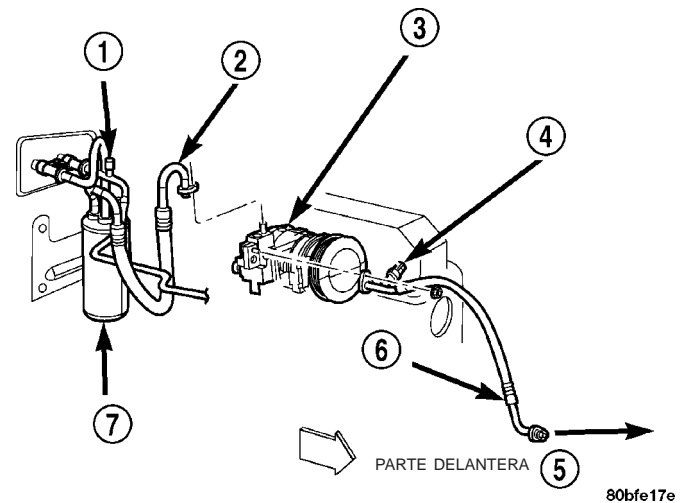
Conductos del compresor - Motor de 4 cilindros
